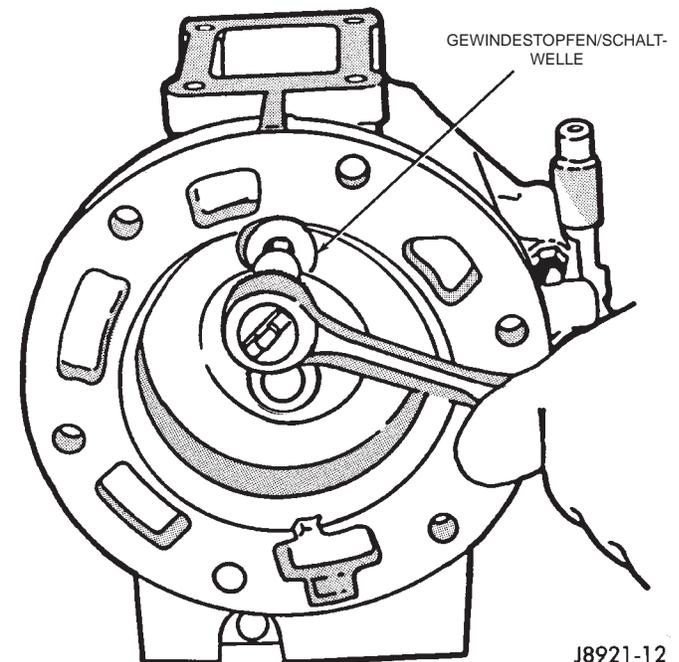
Gewindestopfen der Schaltwelle ausbauen
